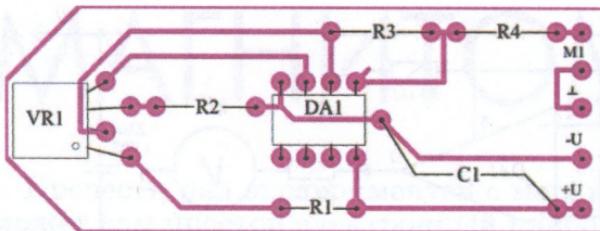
Эскиз монтажной платы прибора. Вид со стороны деталей.
